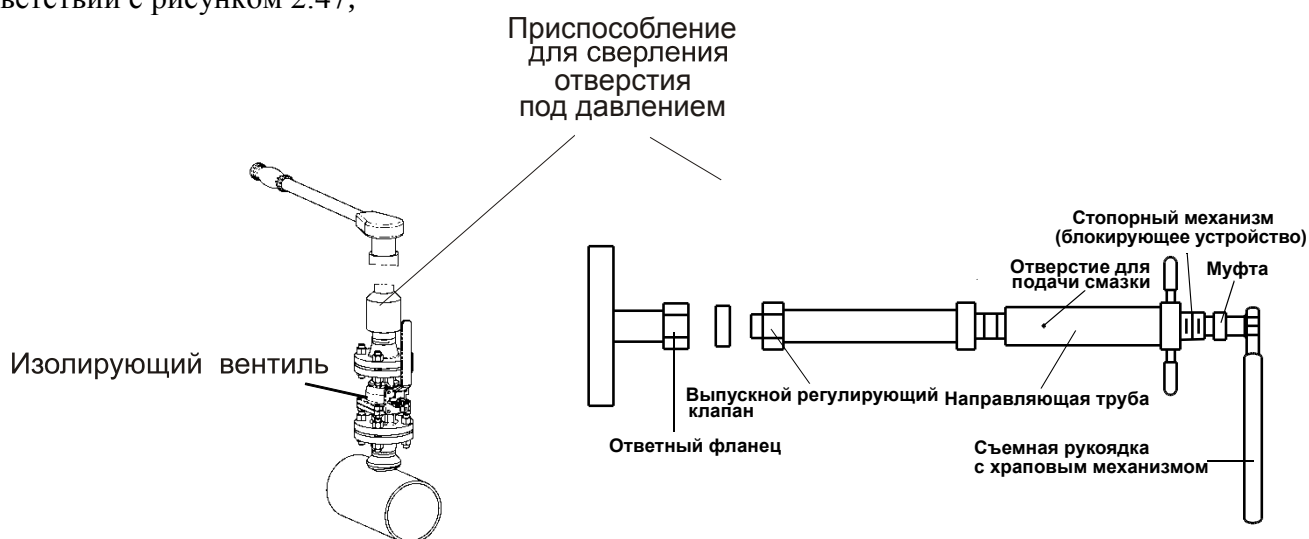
Приспособление для сверления отверстия под давлением на изолирующем вентиле
